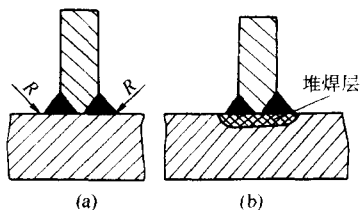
承载件与壳体相焊的接头形式
